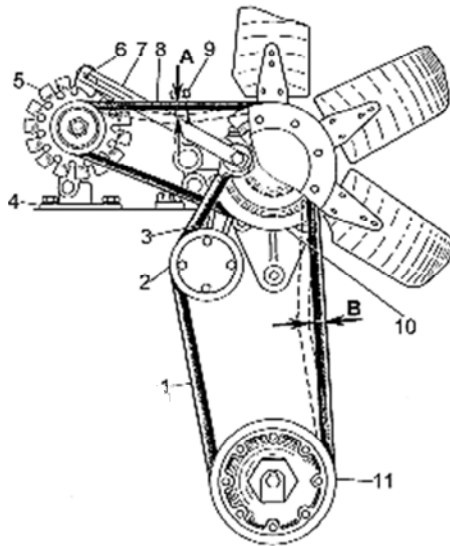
Устройство для натяжения ремней привода вентилятора и генератора двигателей Д-160 и Д-180:
